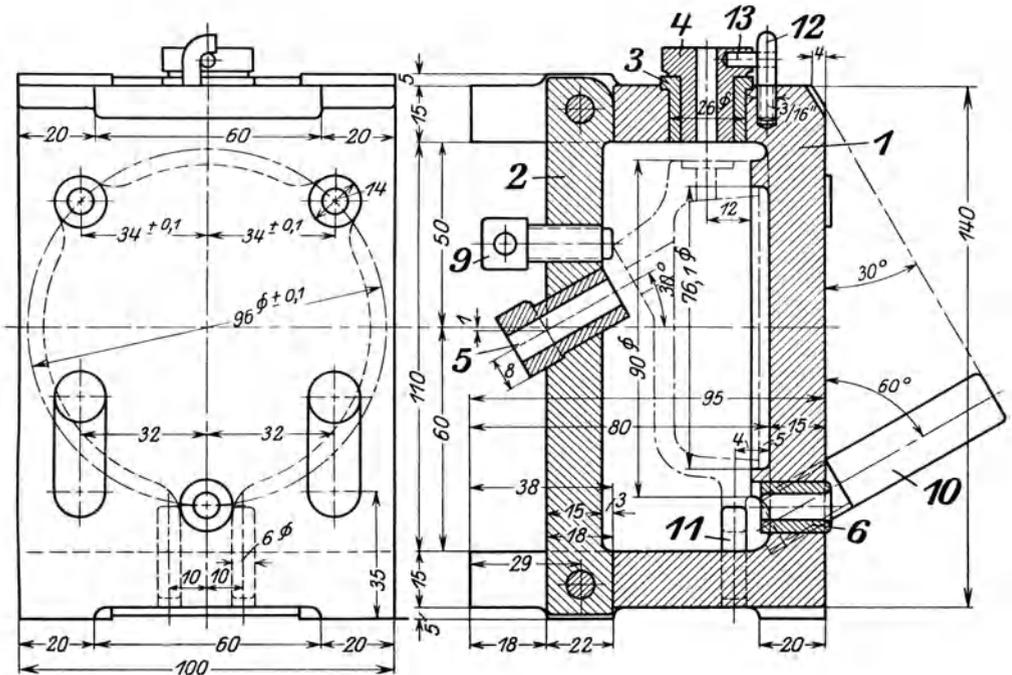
/116. Ausschnitt aus einer Vorrichtung-Zeichnung (Bohrform für einen Deckel).
